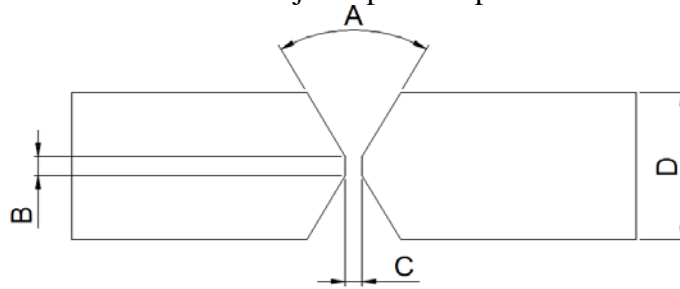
Diseño de junta a tope recomendada para soldadura GMAW/GTAW
